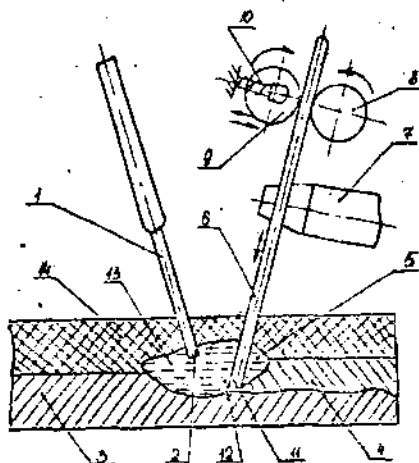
Схема устройства для осуществления способа наплавки с непрерывно расходуемым ультразвуковым волноводом-излучателем: 1 - электродная проволока, 2 - конец электродной проволоки, 3 - наплавляемый образец, 4 - наплавленный металл, 5 - ванна расплавленного металла, 6 - присадочная проволока, 7 - волновод, 8 - приводной ролик, 9 - прижимной ролик, 10 - пружина, 11 - конец волноводной проволоки, 12 - поверхность наплавляемого образца.
